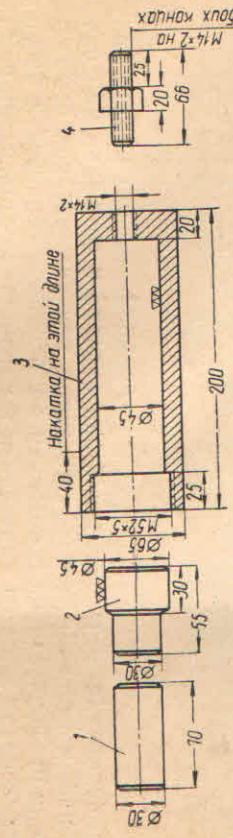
Стакан приспособления для заполнения пресс-форм сырой резиной:
